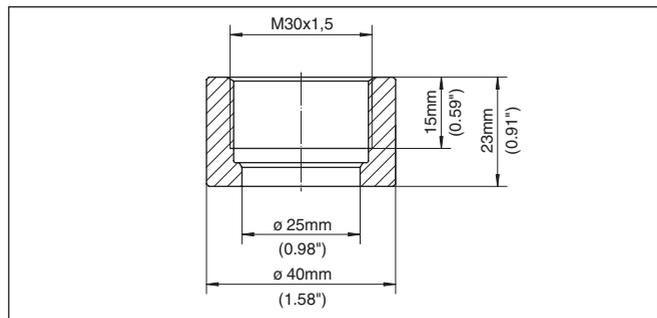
Dimensiones racor para soldar M30 x 1,5 - VEGABAR 82
